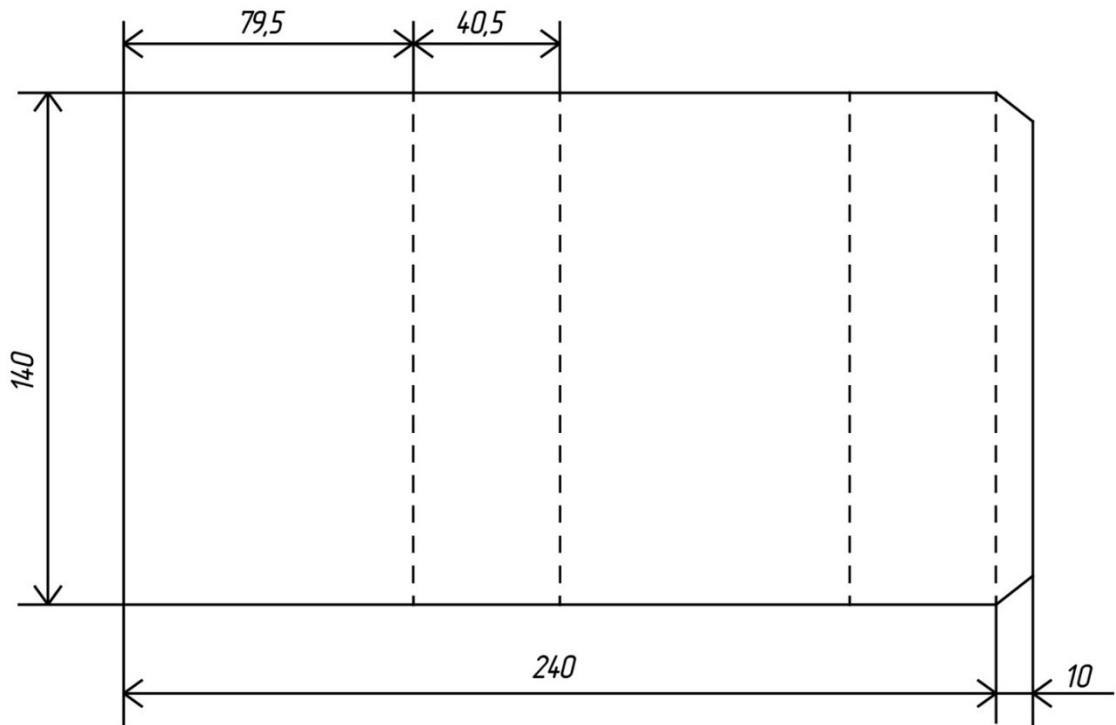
Розгортка зовнішньої частини упаковки пенального типу.
